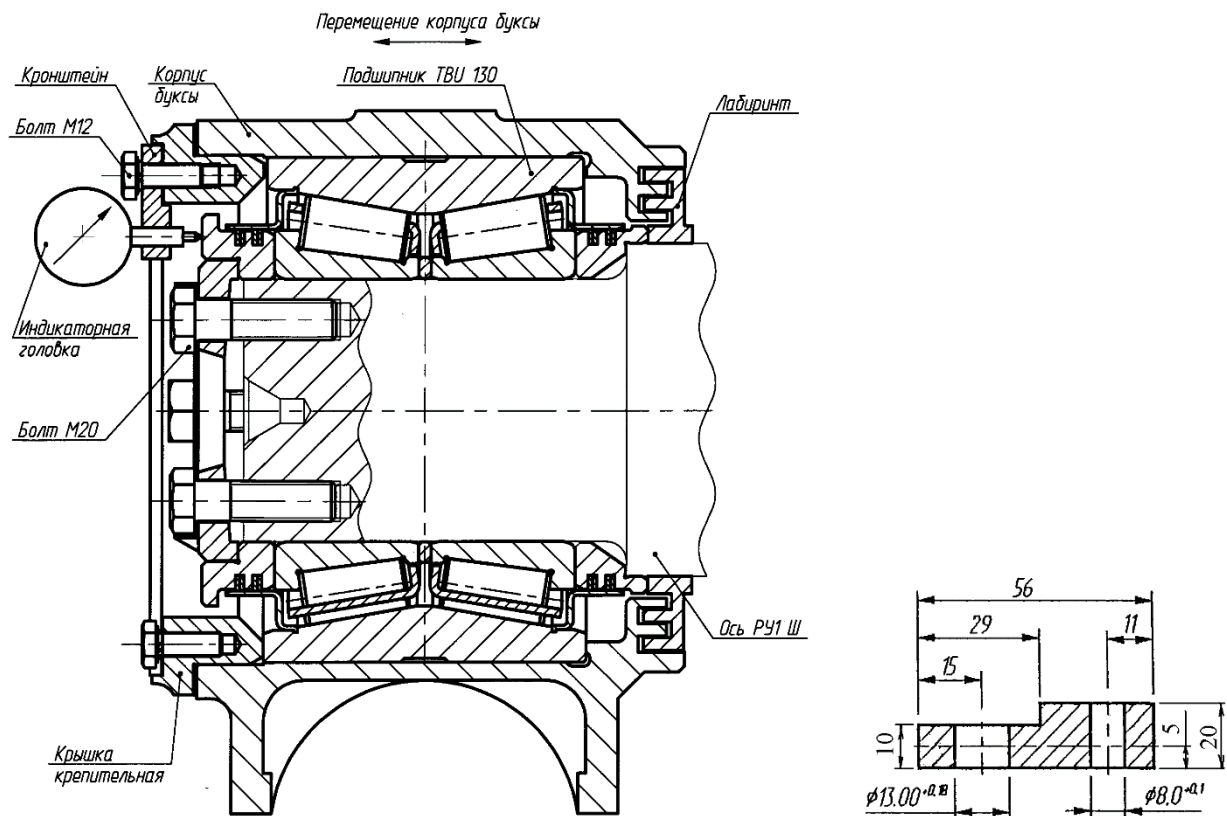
Схема измерения осевого зазора подшипника в габаритах 130x250x160 типа ТВУ 130x250 и кронштейн для установки на крышку при измерении
